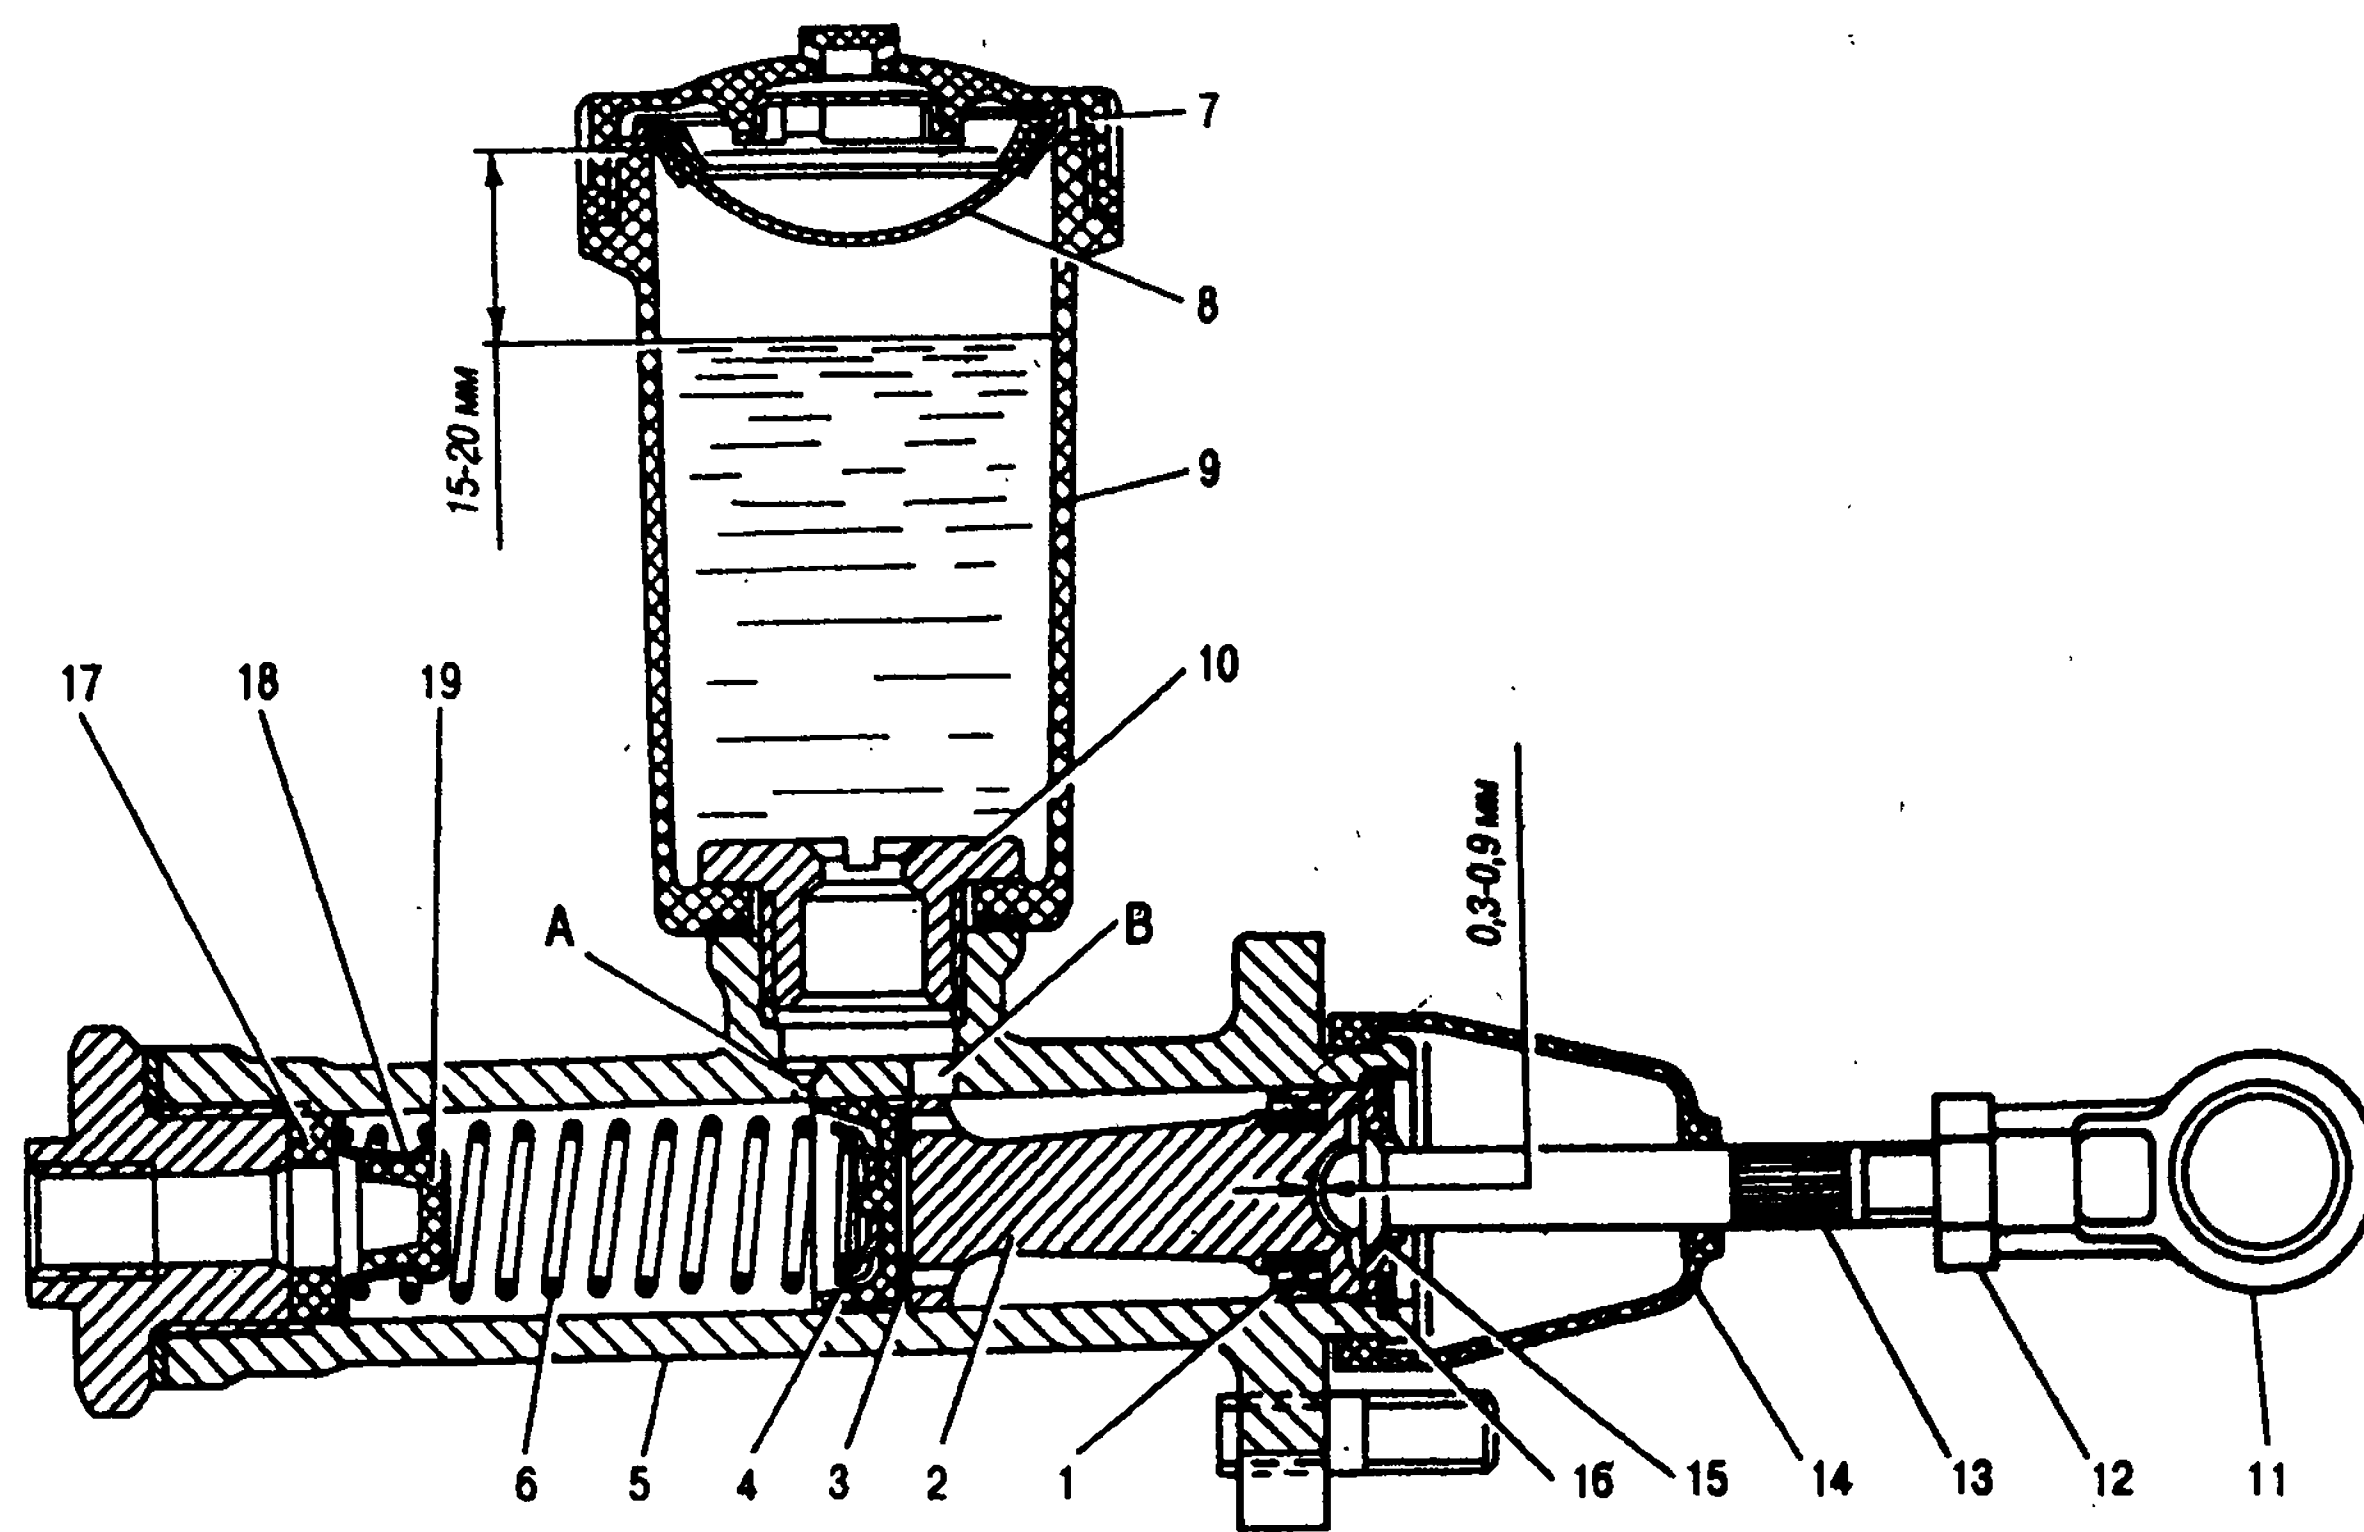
Главный цилиндр привода выключения сцепления: 1, 4 - манжеты; 2 - поршень; 3 - пластинка; 5 - корпус главного цилиндра; 6 - пружина; 7 - крышка; 8 - отражатель; 9 - наполнительный бачок; 10 - штуцер; 11 - проушина; 12 - контргайка; 13 - толкатель рабочего цилиндра; 14 - чехол; 15 - упорная шайба; 16 - стопорное кольцо; 17 - кольцо упорное; 18 - обойма клапана; 19 - клапан; А - компенсационное отверстие; В - перепускное отверстие
